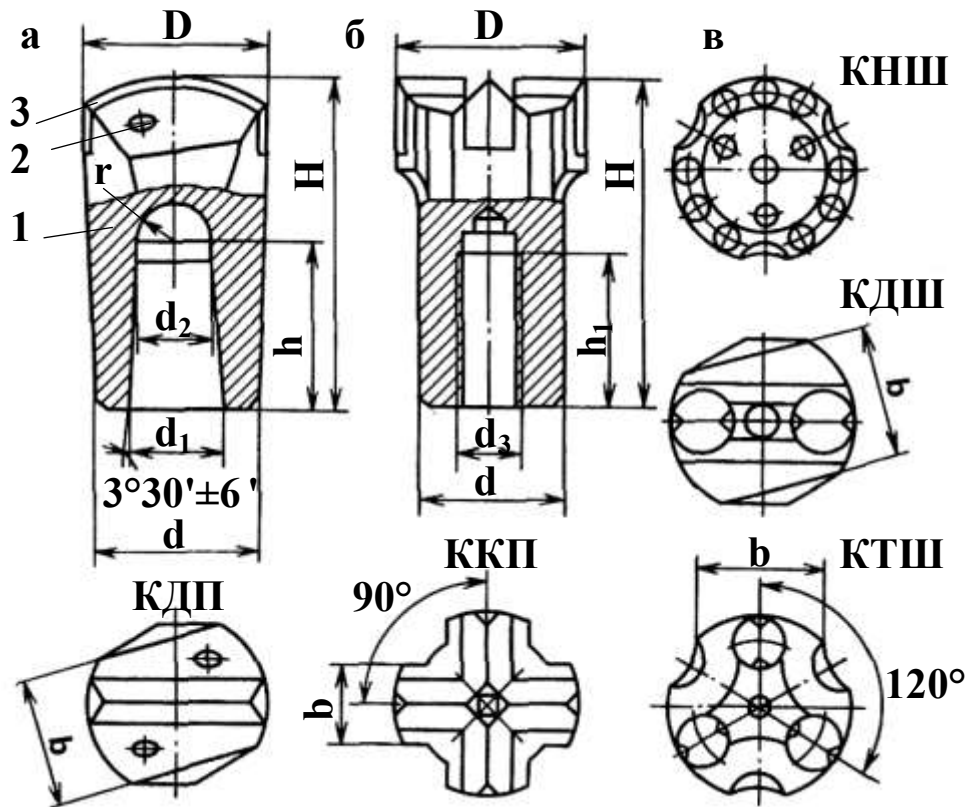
Буровые коронки: а – с конусным отверстием; б – с резьбовым отверстием; в – вид с торца типов КПД; ККП; КНШ; КДШ; КТШ (размеры, мм:  $D$  – диаметр головки,  $d$  – диаметр корпуса,  $d_3$  – диаметр резьбы,  $H$  – высота коронки,  $h_1$  – длина резьбы,  $b$  – толщина лезвия)
